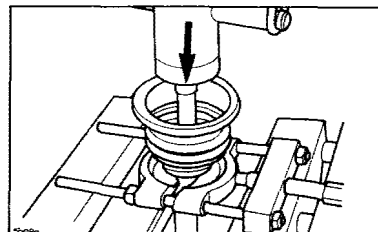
Снятие гофрированного чехла вала привода левого колеса вместе с подшипником с помощью пресса
